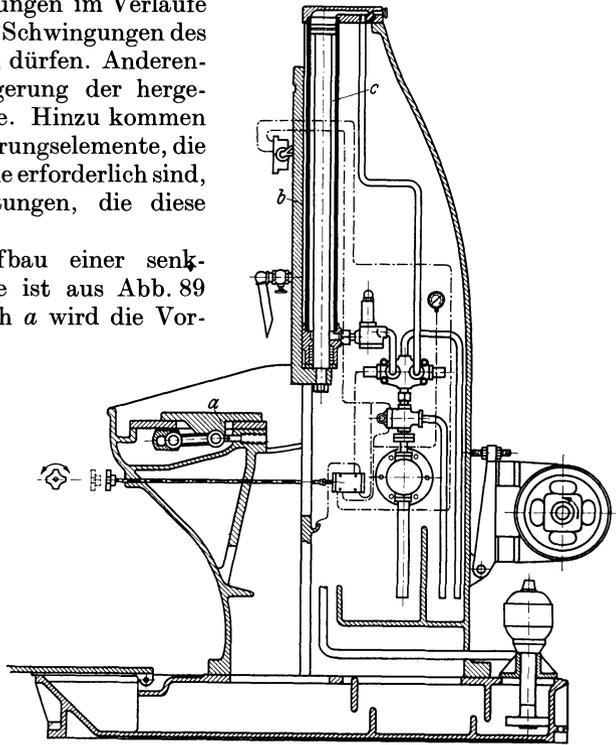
Allgemeiner Aufbau einer Senkrechträummaschine.
